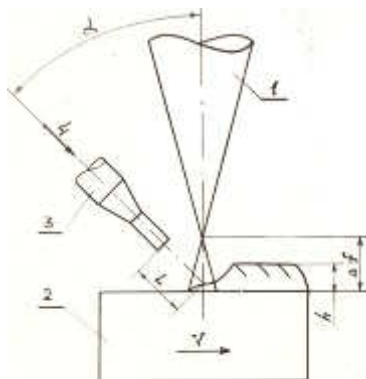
Схема газопорошковой лазерной наплавки: α - угол наклона сопла к оси лазерного луча, V - скорость перемещения образца, L - расстояние сопла до поверхности образца, Δf - степень расфокусировки, h - высота наплавленного валика, 1 - луч лазера, 2 - образец, 3 - сопло, 4 - подача порошка.
